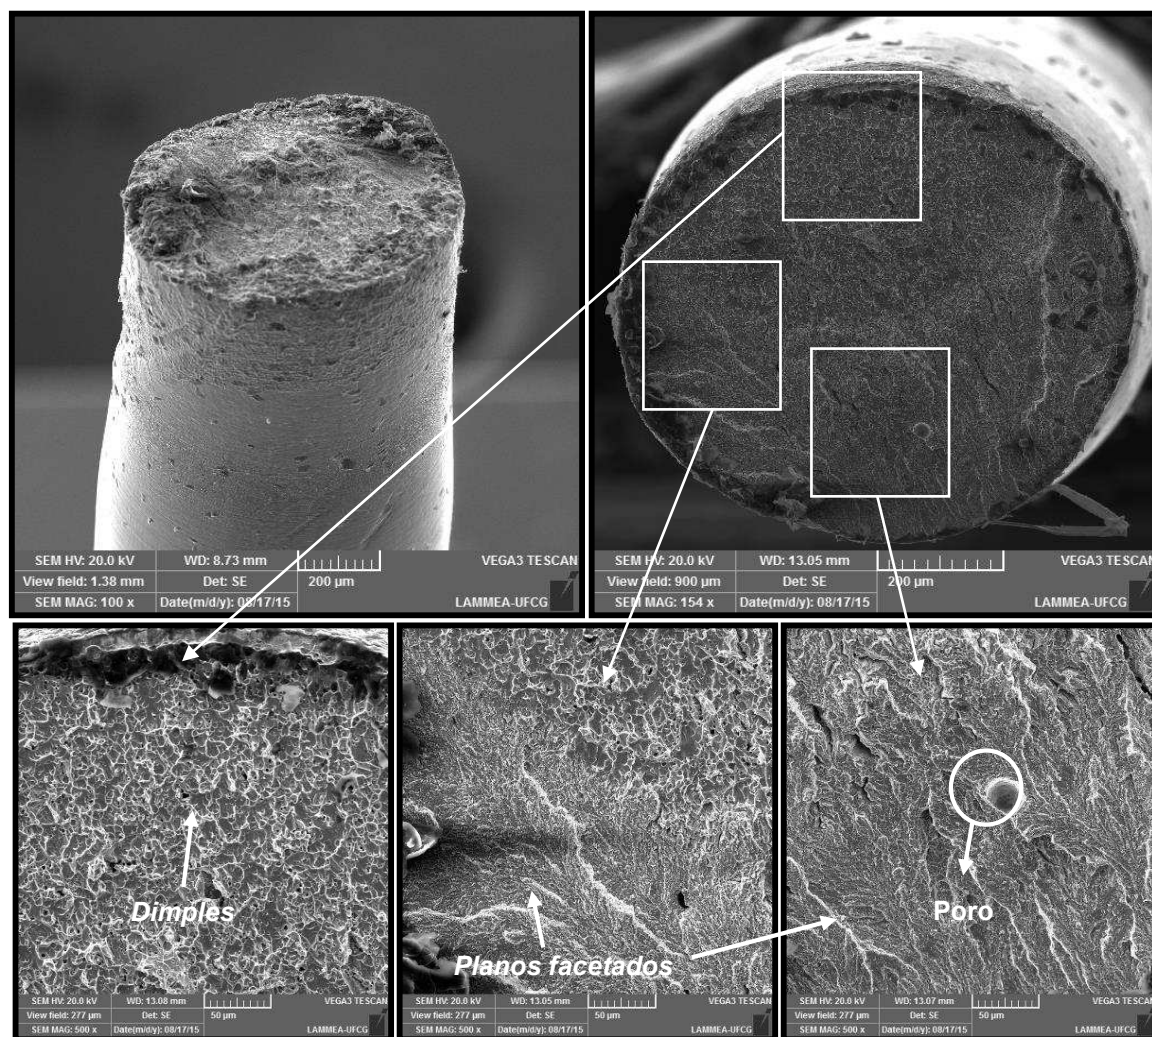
Superfície de fratura do fio atuador soldado na configuração 7ms/70% e testado a 90°C.
